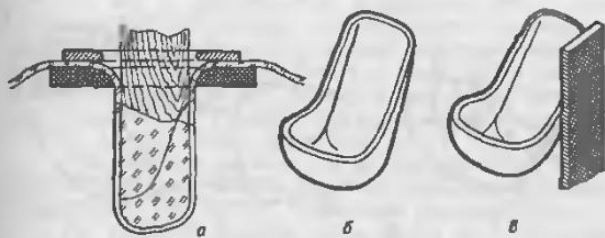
Последовательность изготовления сиденья штамповкой из листового пластика: а - штамповка; б - обрезка заготовки; в - опиливание готовой детали
